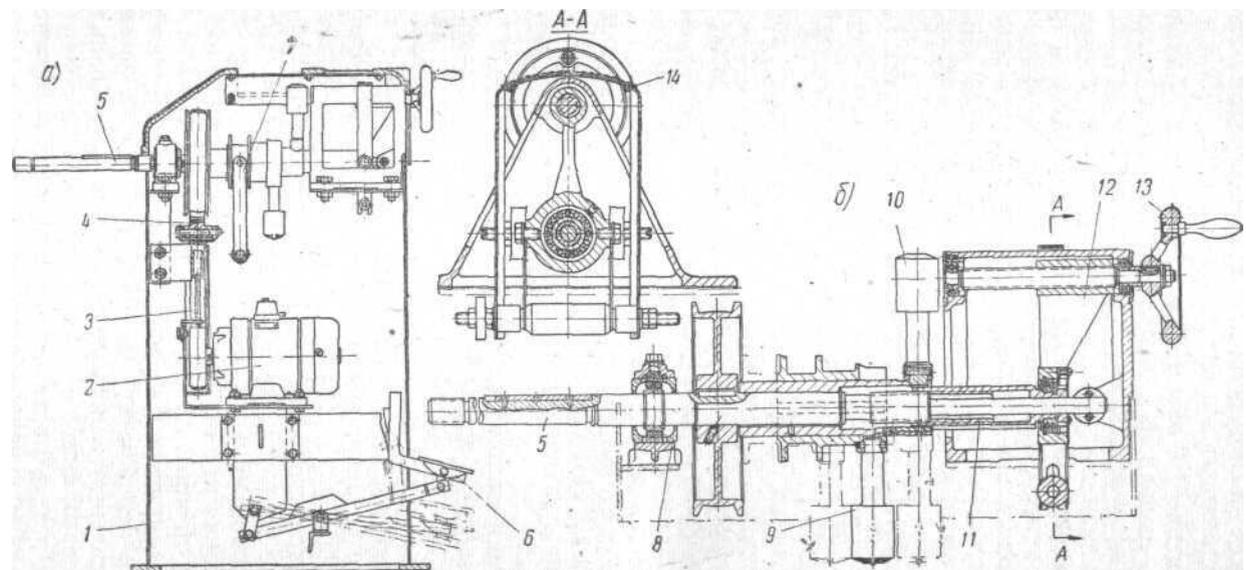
Станок для статической балансировки колес в сборе с шинами:
